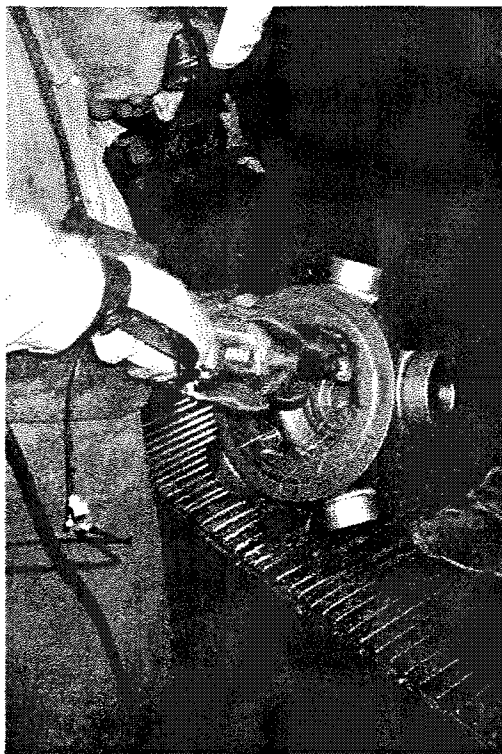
Addetto alla sbavatura delle parti cave dei getti
